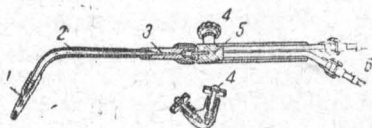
Ацетилено-кислородная сварочная горелка типа СУ-48
